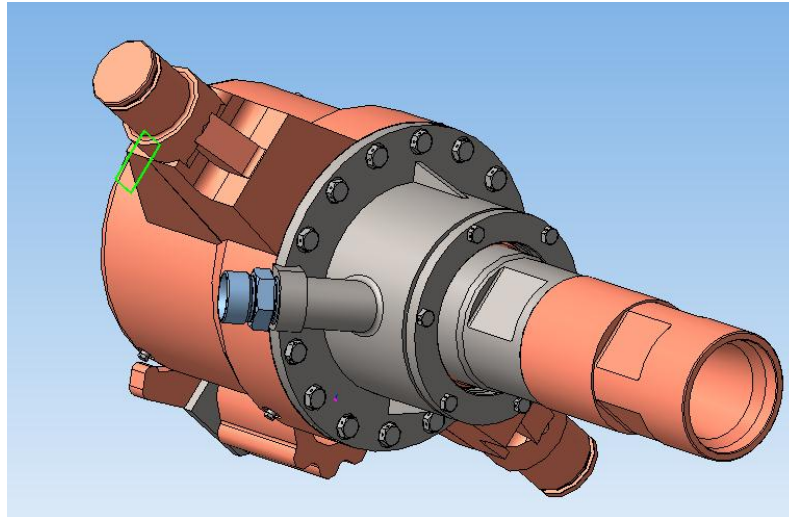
Вузол опорний верстату СБШ-250МНА-32 (3D)
